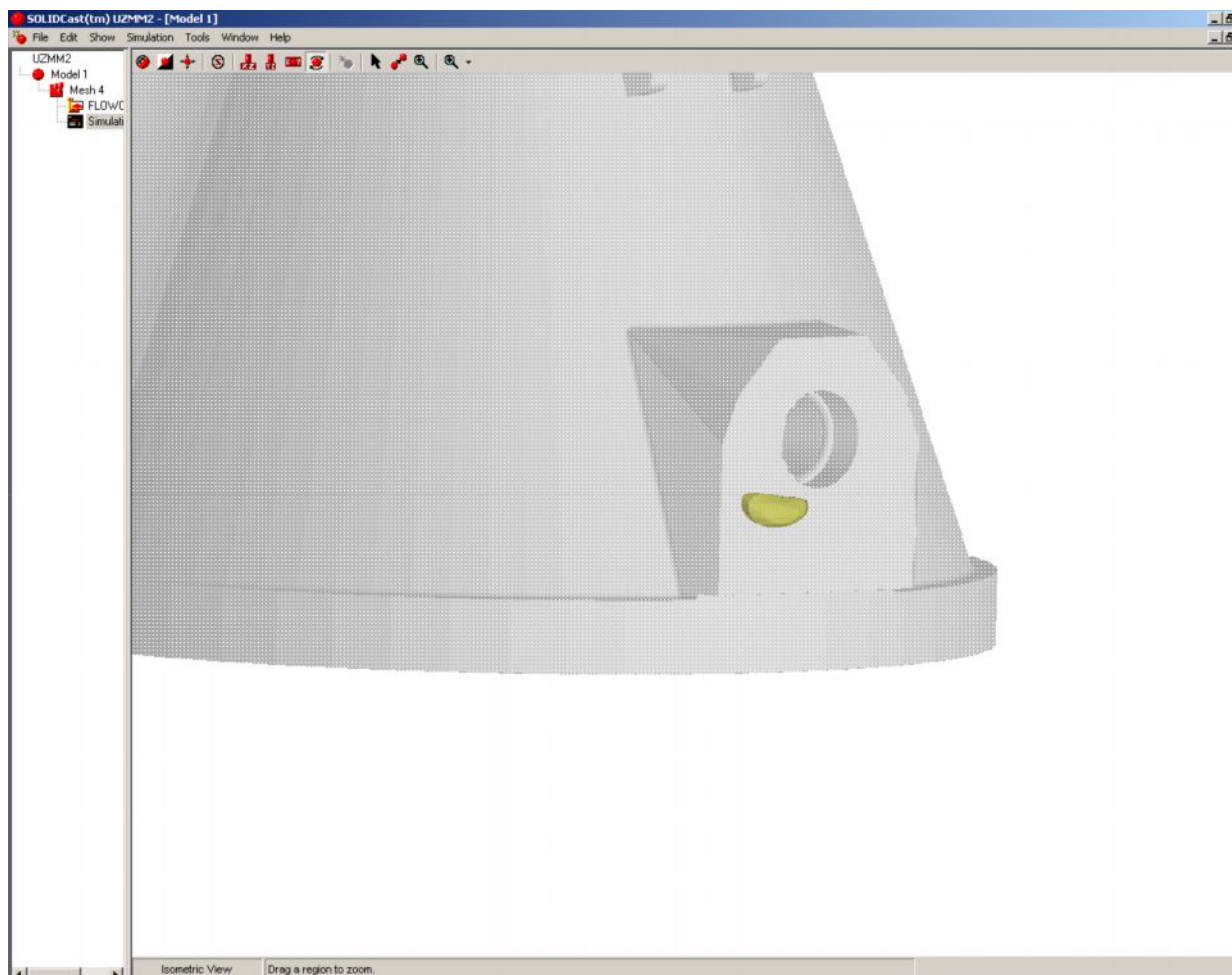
Усадочные дефекты в отливке “Чаша”
